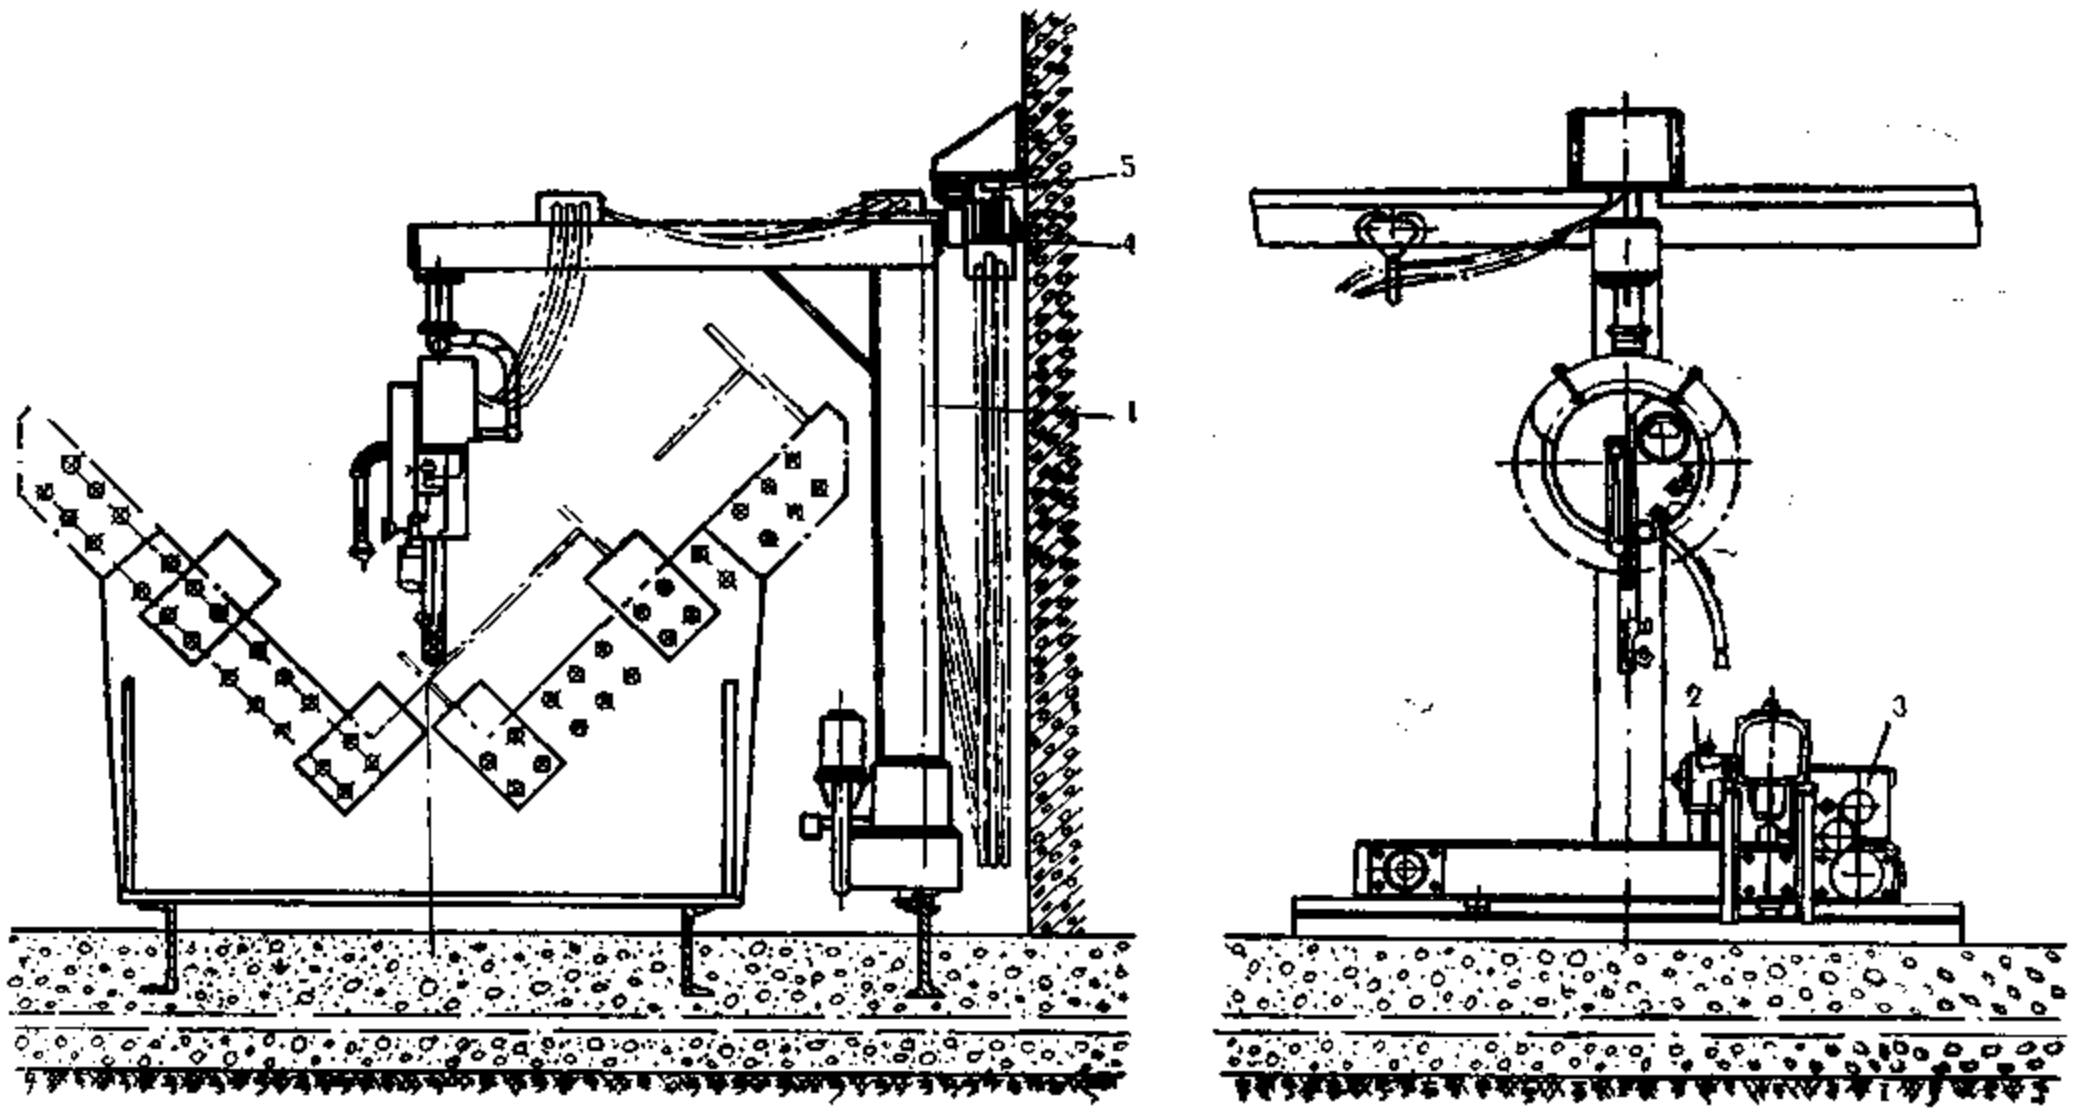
焊接工字梁纵缝的悬臂架式操作机
